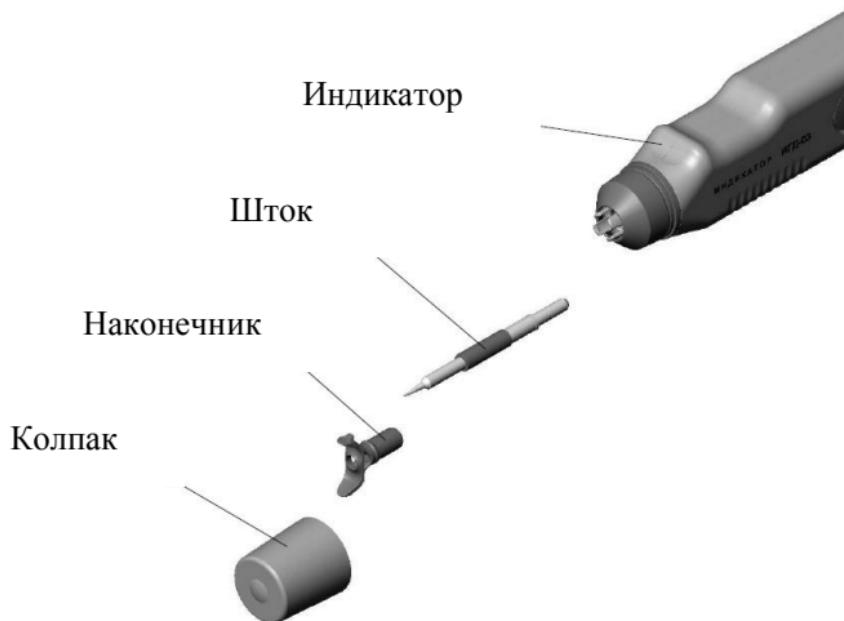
Подготовка индикатора к очистке штокового механизма
